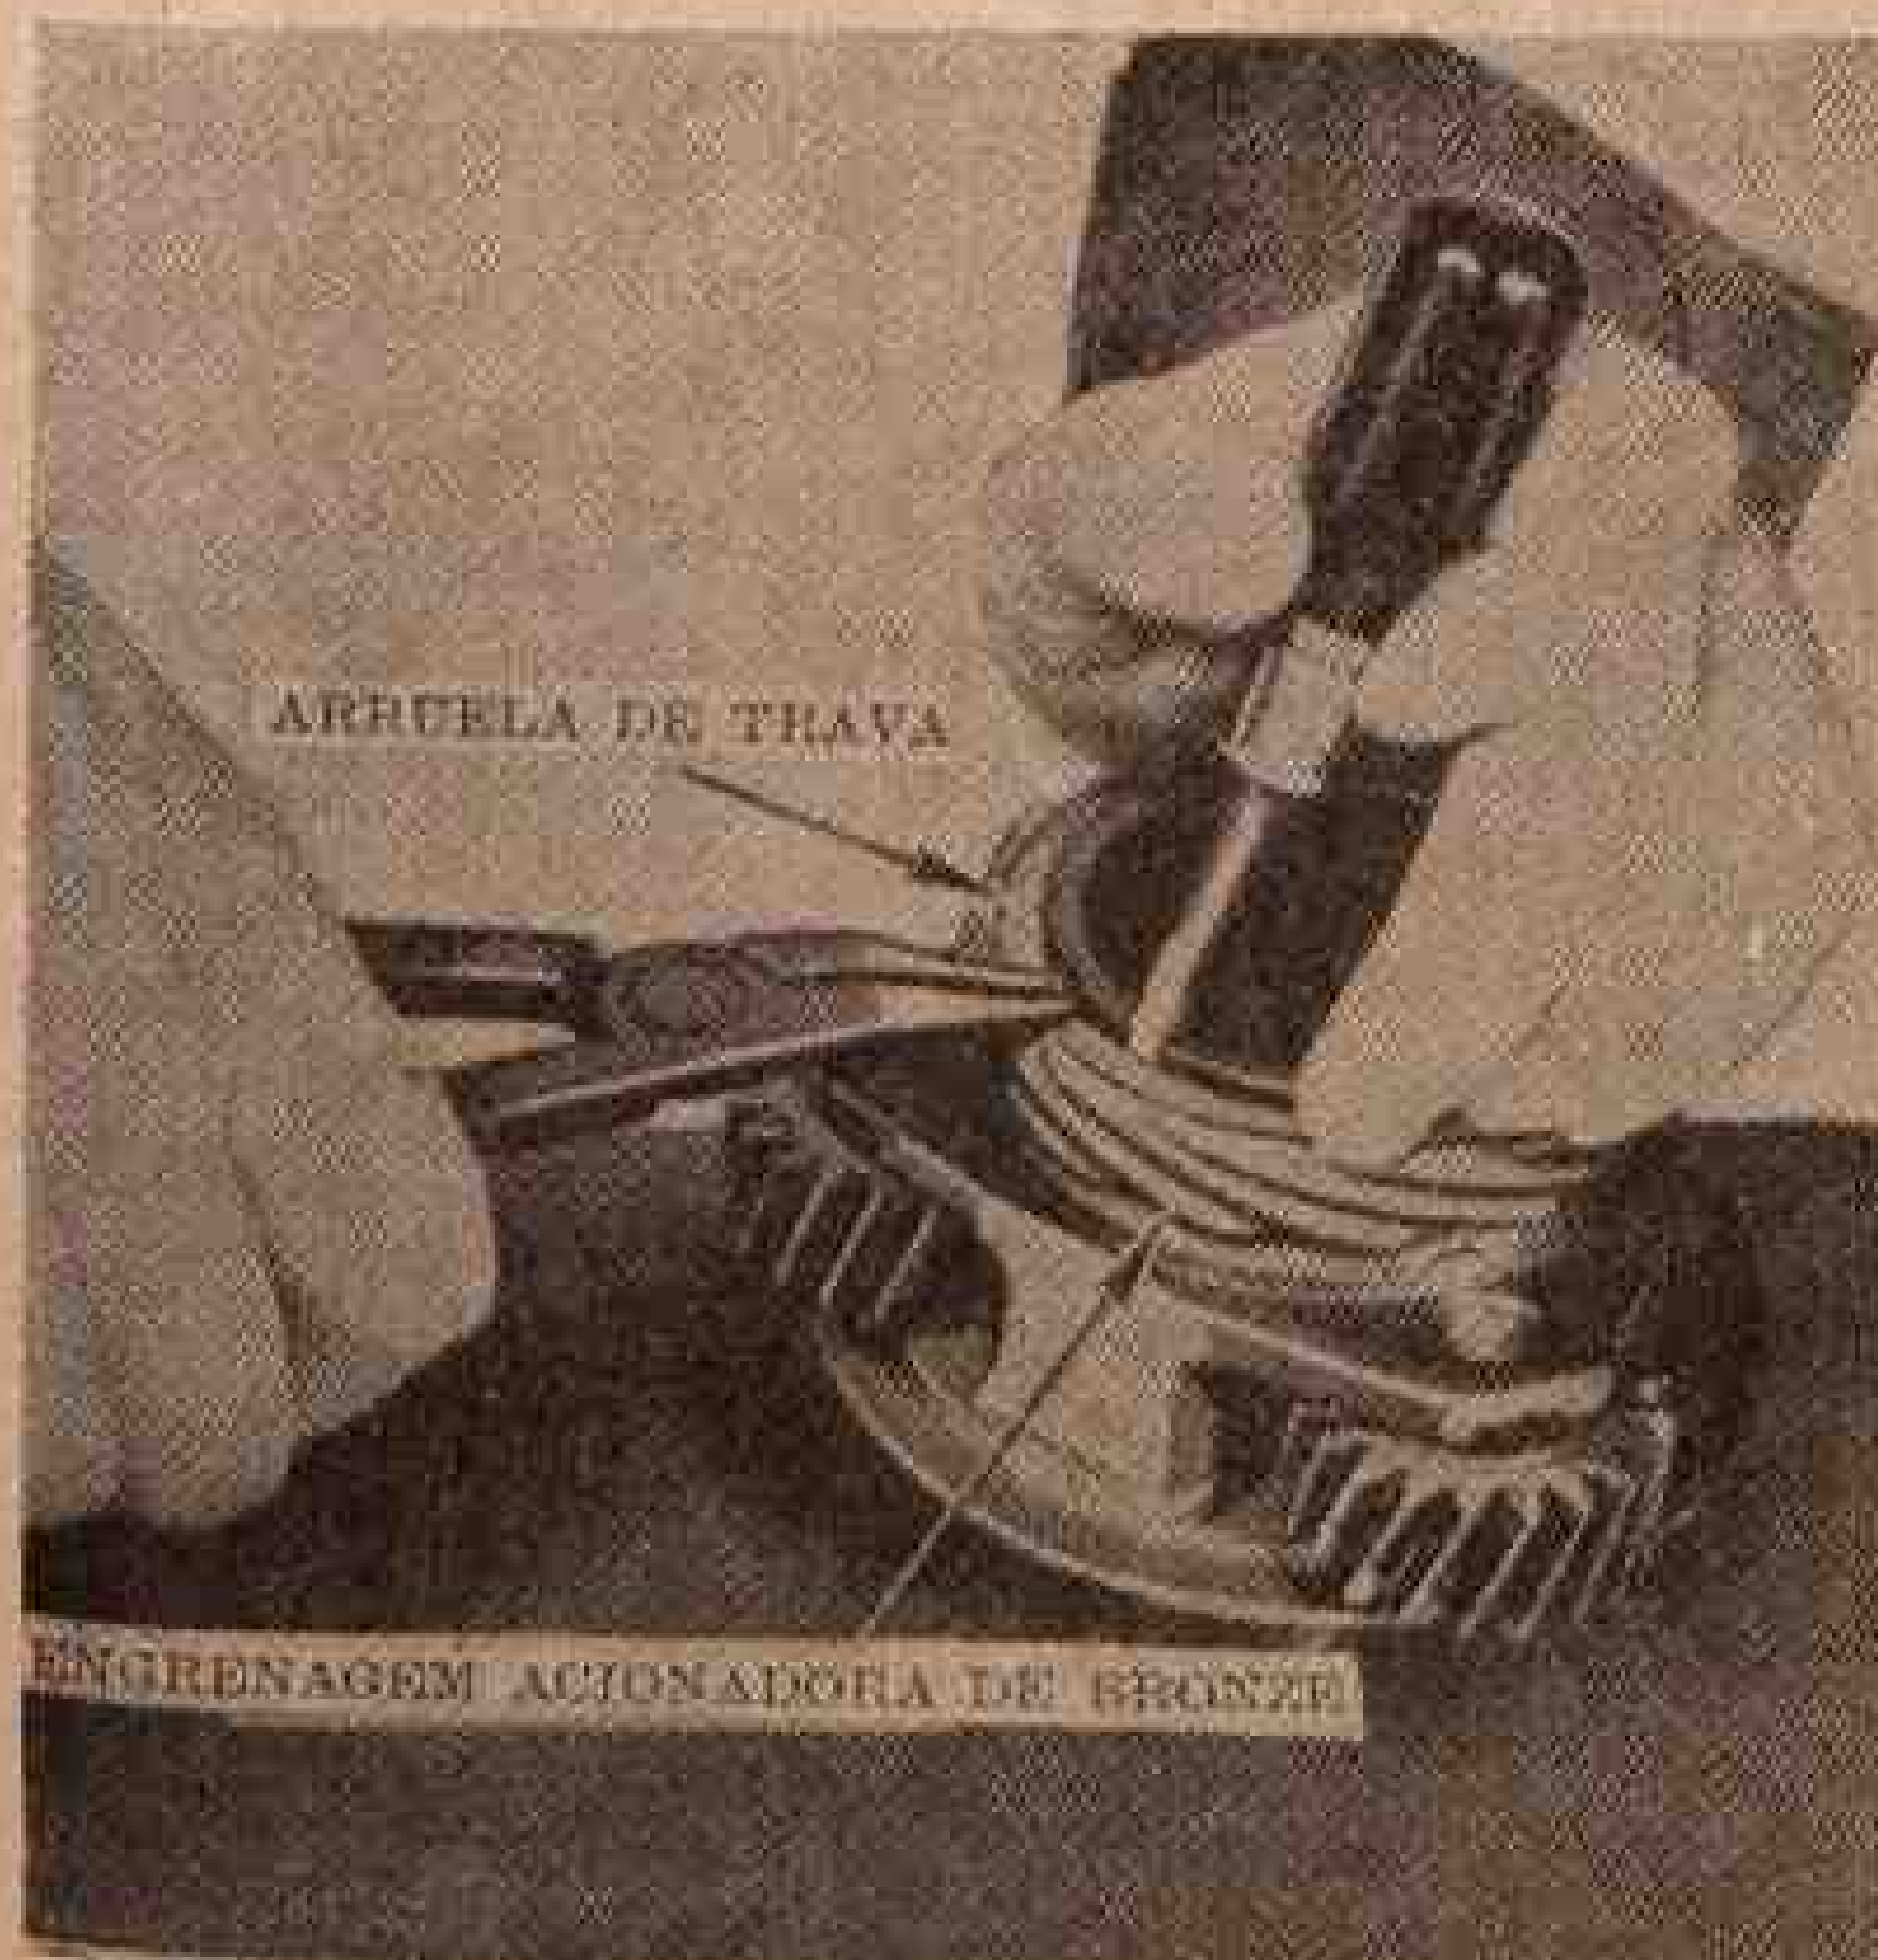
Removendo a bomba de óleo e a arruela de trava da engrenagem do governador
